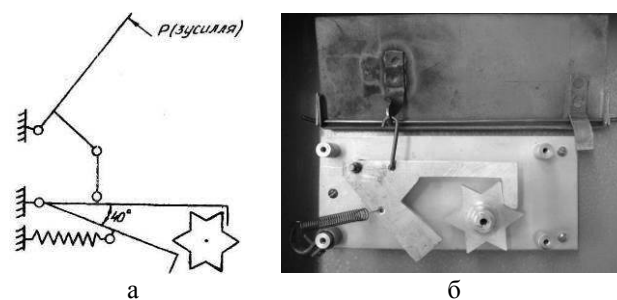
Обліковий механізм ФКЗ: а – кінематична схема; б – зовнішній вигляд
